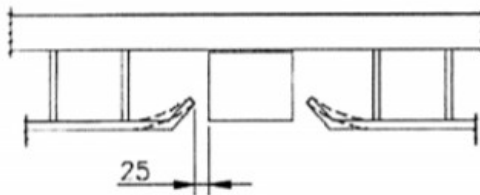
, Holgura con componentes del vehículo, Vista Superior (dimensiones en mm)
